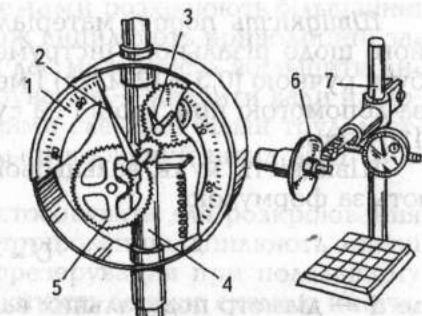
Індикатор для перевірки осового биття пилкової шайби:
